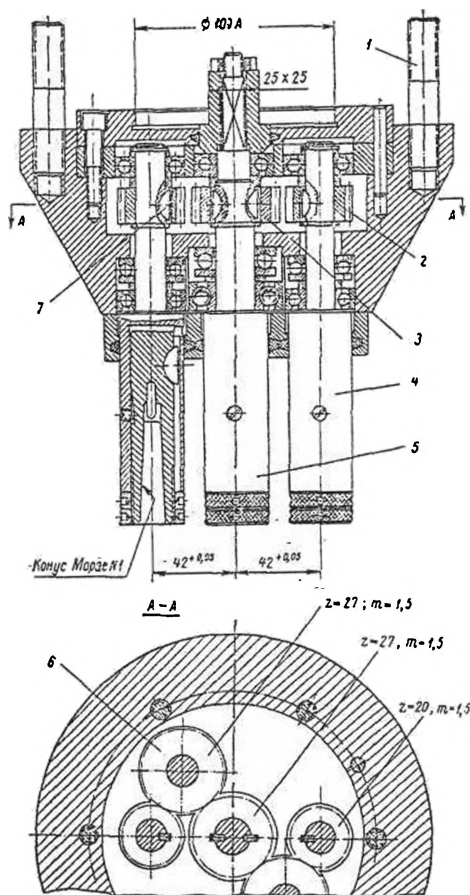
Трьохшпиндельна свердлильна головка з одноярусним розташуванням зубчатих коліс для обробки отворів, що розташовані в лінію
